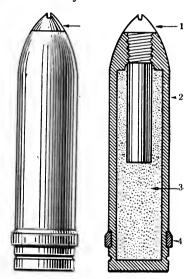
Граната. 1— взрыватель; 2— стальной корпус; 3— разрывной заряд; 4— ведущий пояс.
